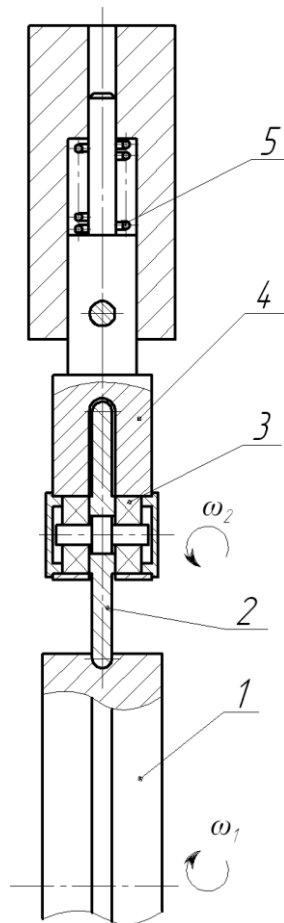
Схема зміцнення поверхневого шару зовнішньої канавки на циліндричній поверхні пластичним деформуванням методом обкатування циліндричним роликом: 1 – заготовка із попередньо проточеною канавкою; 2 – ролик для обкатування; 3 – підшипники кочення; 4 – кронштейн; 5 – пружина
